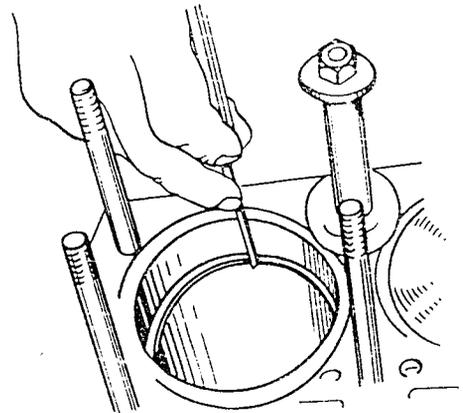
Anpassung der Kolbenringe an dem Zylinder (Prüfung des Seitenspiels im Ringschloß)
